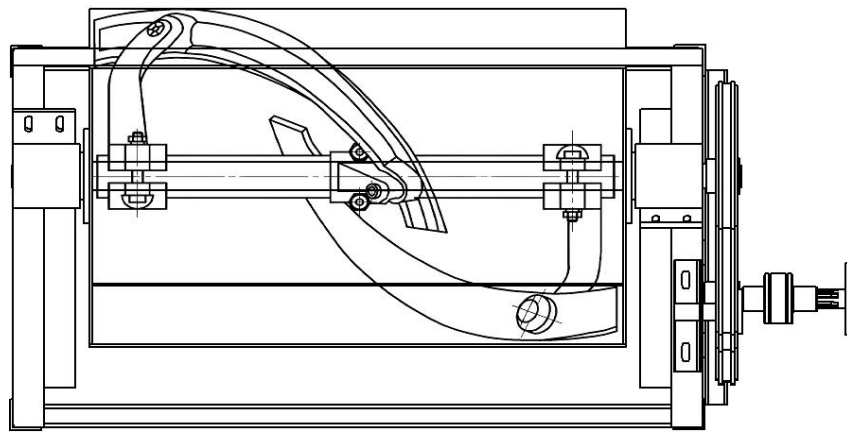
Схема розчинозмішувача, вигляд згори
